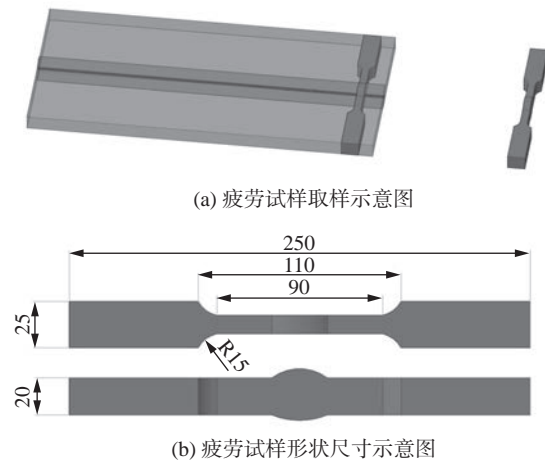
疲劳试样取样以及形状尺寸示意图 (mm)
